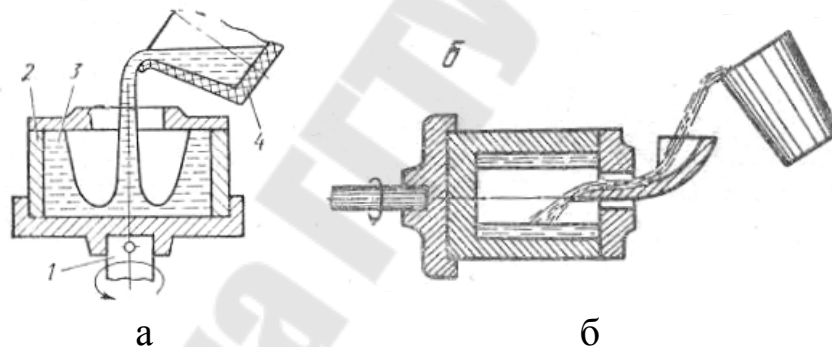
Центробежное литье: а – с вертикальной осью вращения формы; б – с горизонтальной осью вращения формы; 1 – привод; 2 – литейная форма; 3 – расплавленный металл; 4 – разливочный ковш
